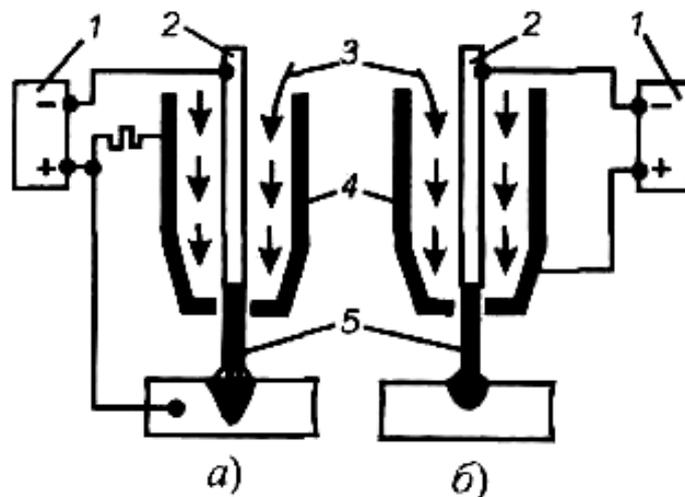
Схемы получения дуговой плазменной струи:
